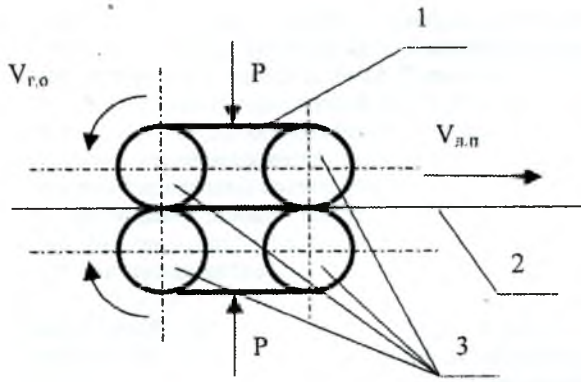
Схема конструкции ленточно-конвейерных направляющих ленточнопильного станка на основе длинных контактов трения относительного покоя:
